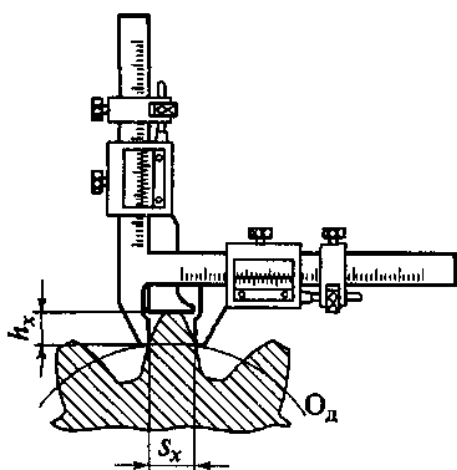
Измерение толщины зуба колеса цилиндрической передачи:
